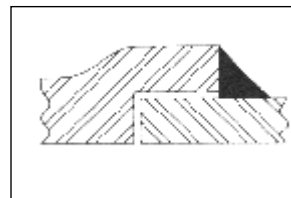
Soldadura de enchufe - corrosión severa
